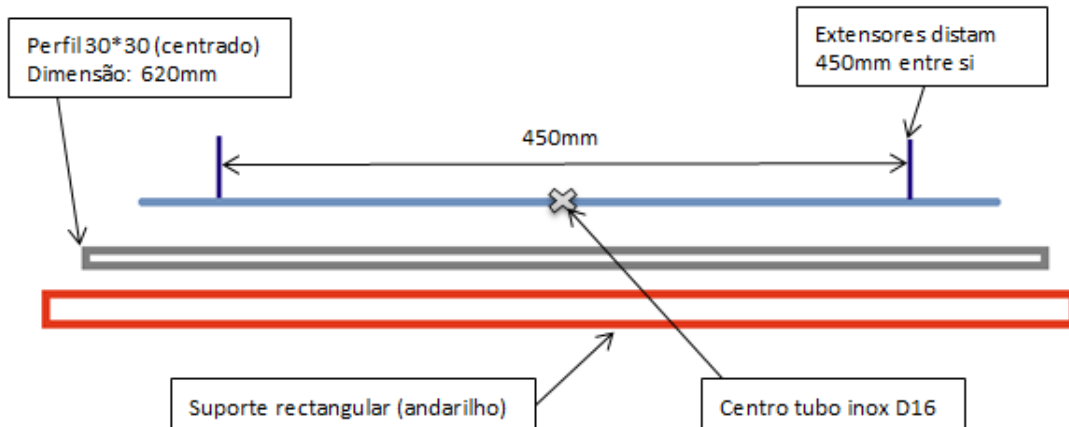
Esquema representativo das dimensões e posição dos componentes no guiador
